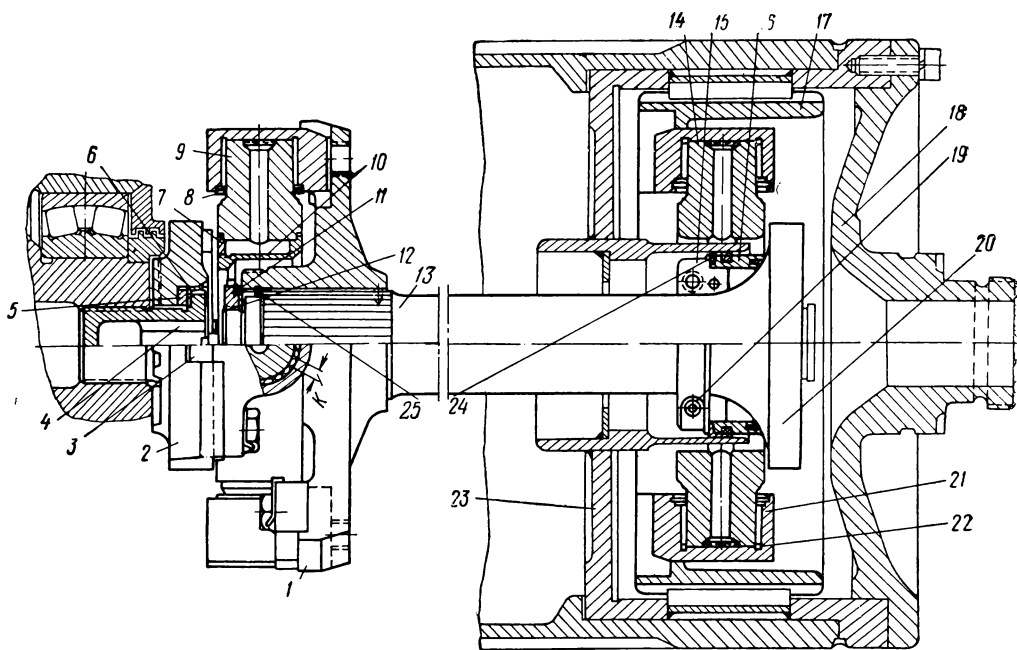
Привод тягового двигателя электровоза ЧС2:
